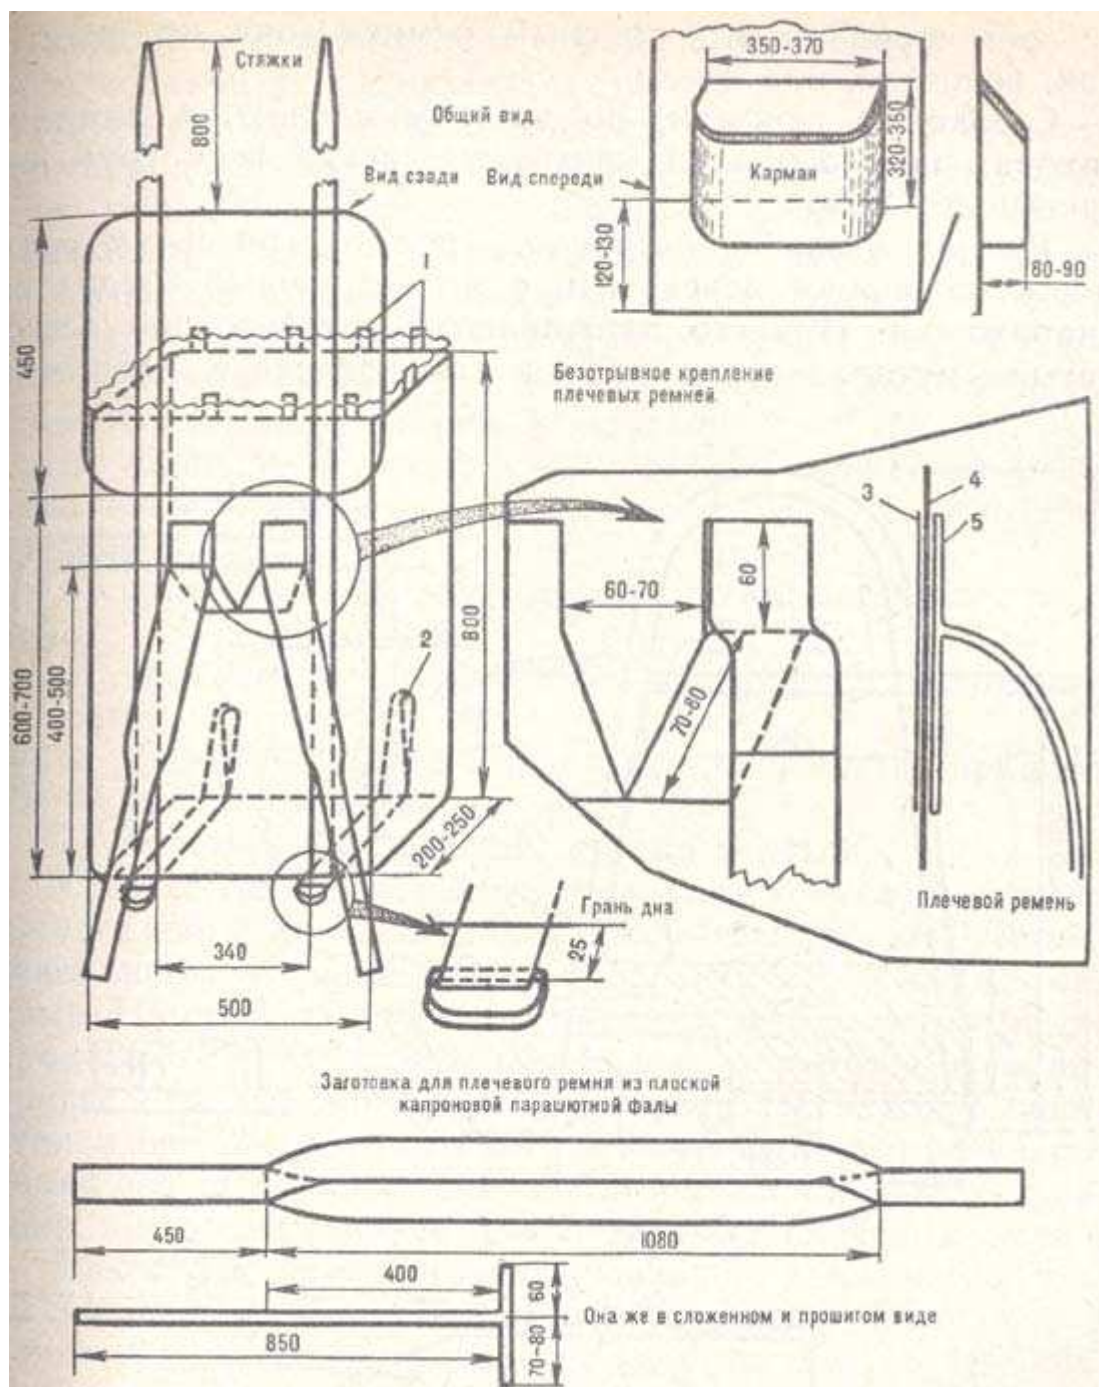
Рюкзак мягкой конструкции: 1 - петли для шнура, стягивающего верх; 2 — петли для привязывания стяжек; 3 — ткань усиления; 4 — ткань рюкзака; 5 — противоотрывный пришив плечевых ремней.
